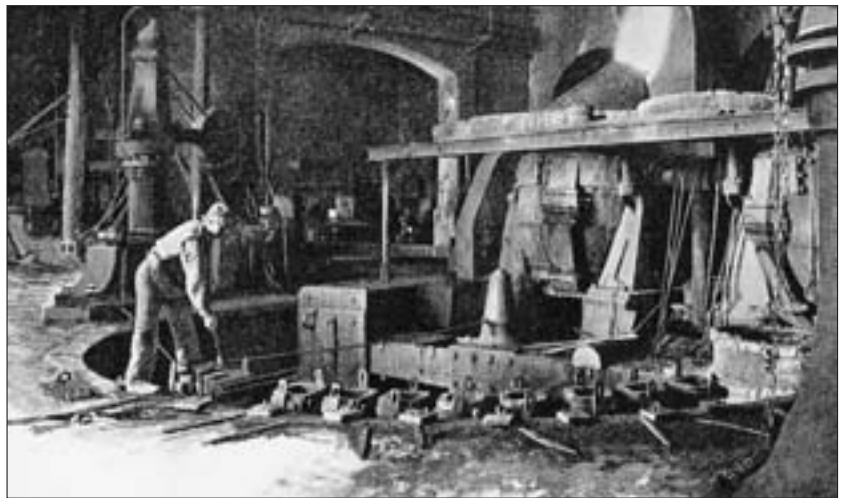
Bessemerstahlwerk in Heft um 1880 (?). Rechts der Bildmitte einer der beiden 1870/71 installierten 7-t-Konverter; links und im Vordergrund runde Gießgrube mit Kokillen für Blockguss; von dem mit Druckwasser betriebenen Gießkran am rechten Bildrand ist nur wenig zu sehen. Aufnahme aus Wolff, V.: Die Montan-Industrie Österreichs. In: Die Groß-Industrie Österreichs. Wien 1898, S. 171-236, Bild auf S. 199.
